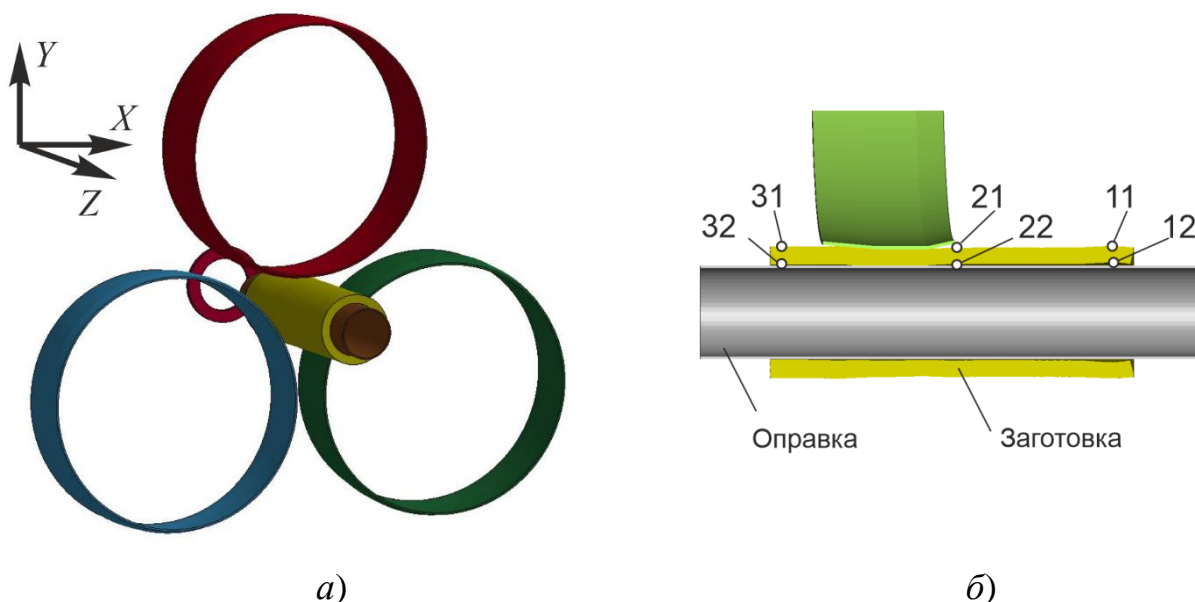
Положение заготовки на заключительной стадии ПВП (а) и положение узлов на внешней и внутренней поверхности заготовки для анализа НДС (б)
